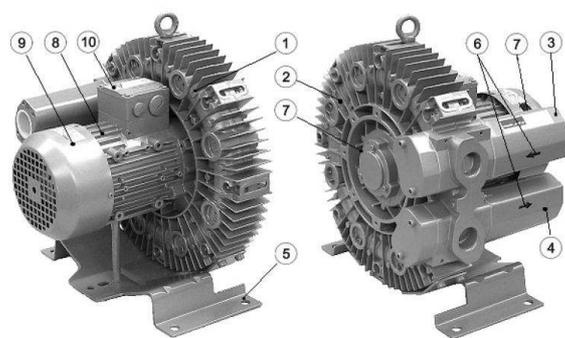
Конструкция вихревой воздуховулки (вакуумного насоса/компрессора)
